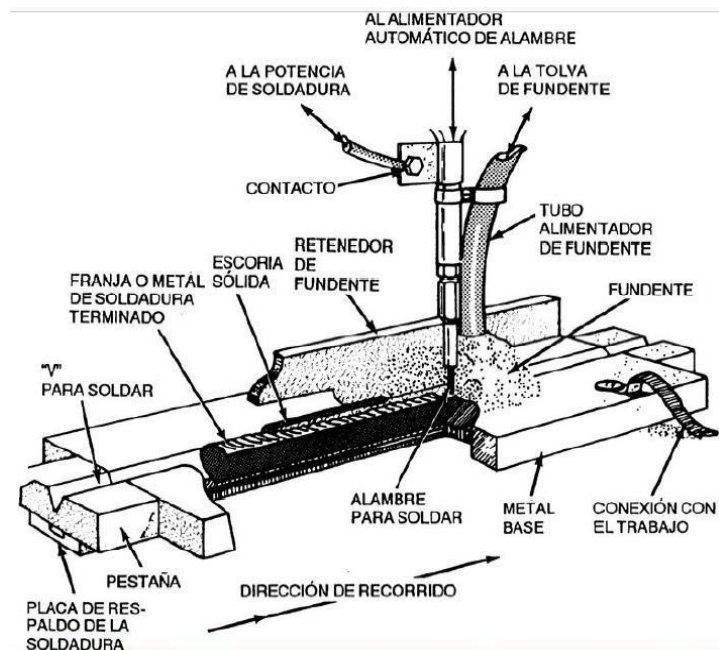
Proceso de soldadura en Arco Sumergido SAW.
